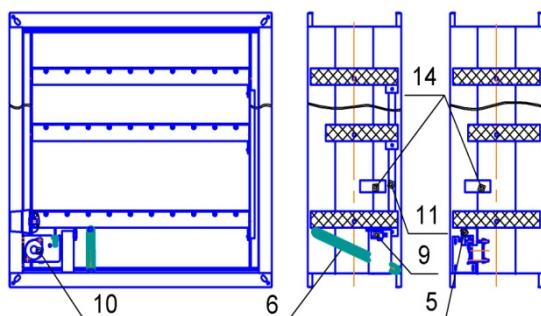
Установочные, габаритные и размеры внутреннего сечения клапана.
